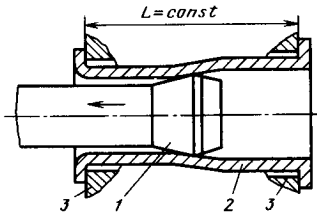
Обработка с осевым заневоливанием детали: 1 — инструмент; 2 — деталь; 3 — опоры
